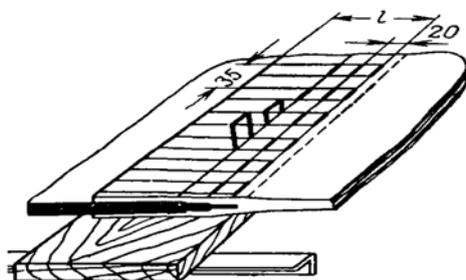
Скрепление концов ленты П-образными скобами [2]
